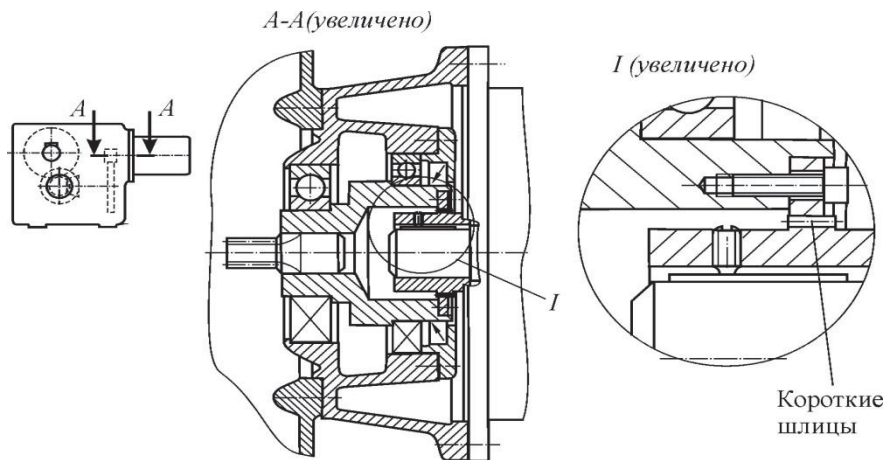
Соединение валов двигателя и редуктора мотор-редуктора фирмы Swedrive короткими шлицами
